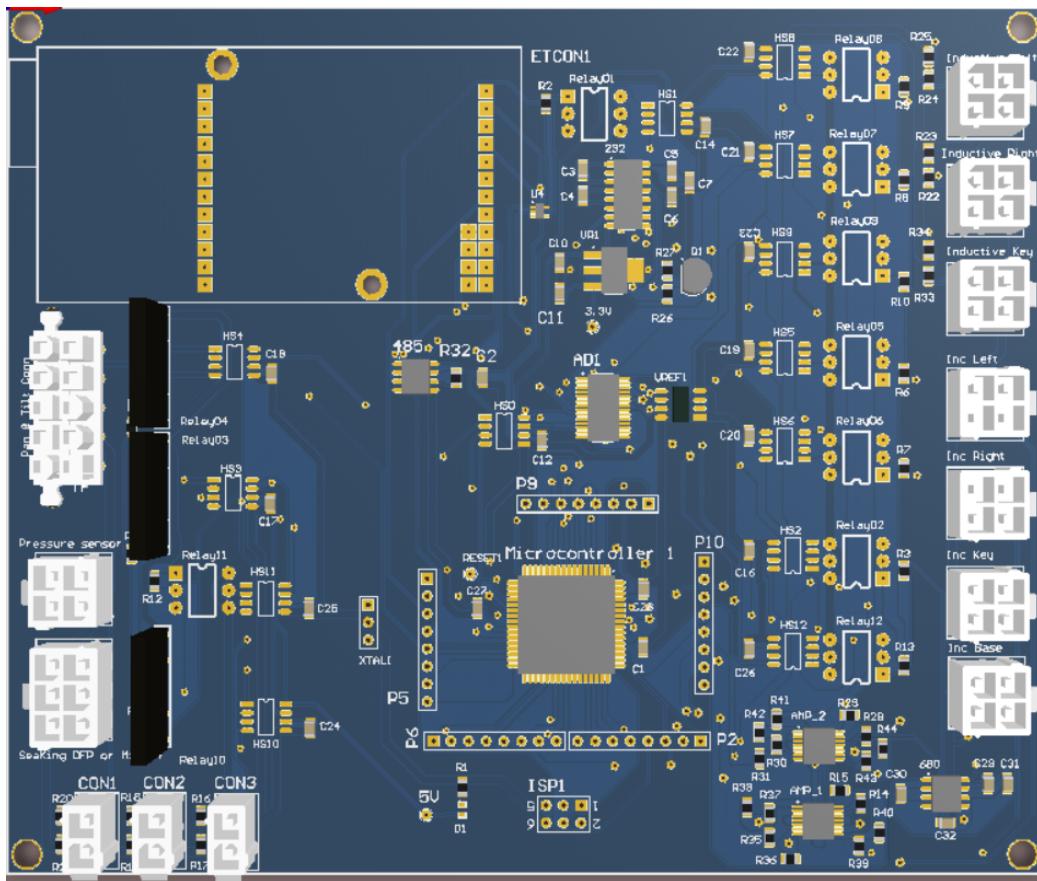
Placa 3D - versão com sensores de inclinação com condicionamento de sinal
